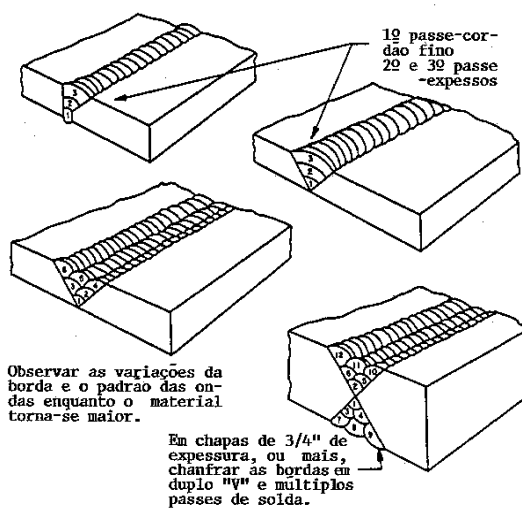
Múltiplos passes de solda em junta de topo chanfrada.
